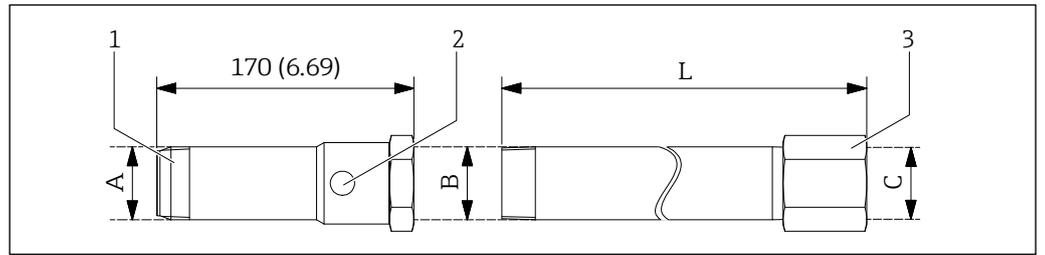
Dimensiones boquilla soldada. Unidad de medida mm (in)
